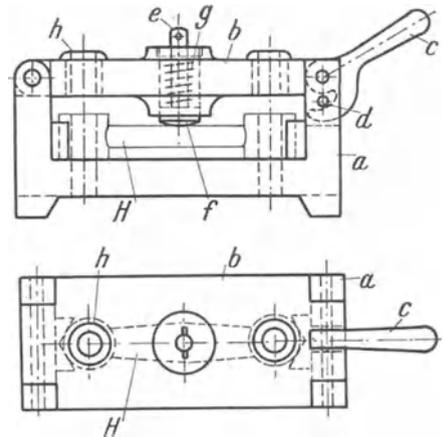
Standbohrspannvorrichtung mit schlechter Wirkungsweise.
